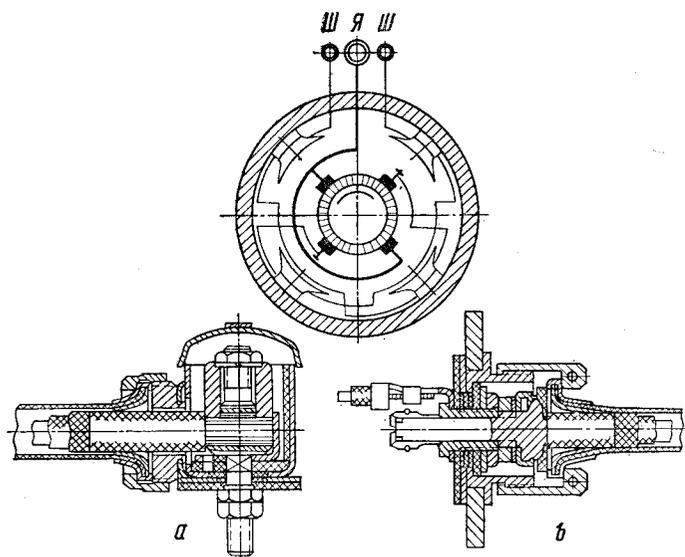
Схема подсоединения проводов к генератору Г-731А:
